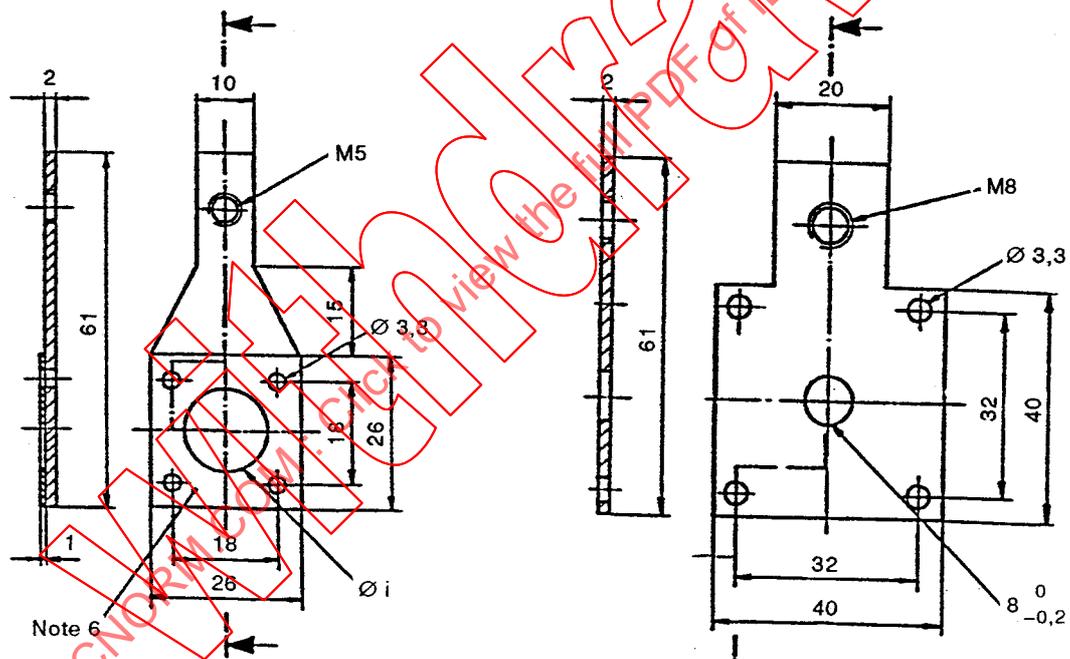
Dispositifs d'essai pour éléments de remplacement
